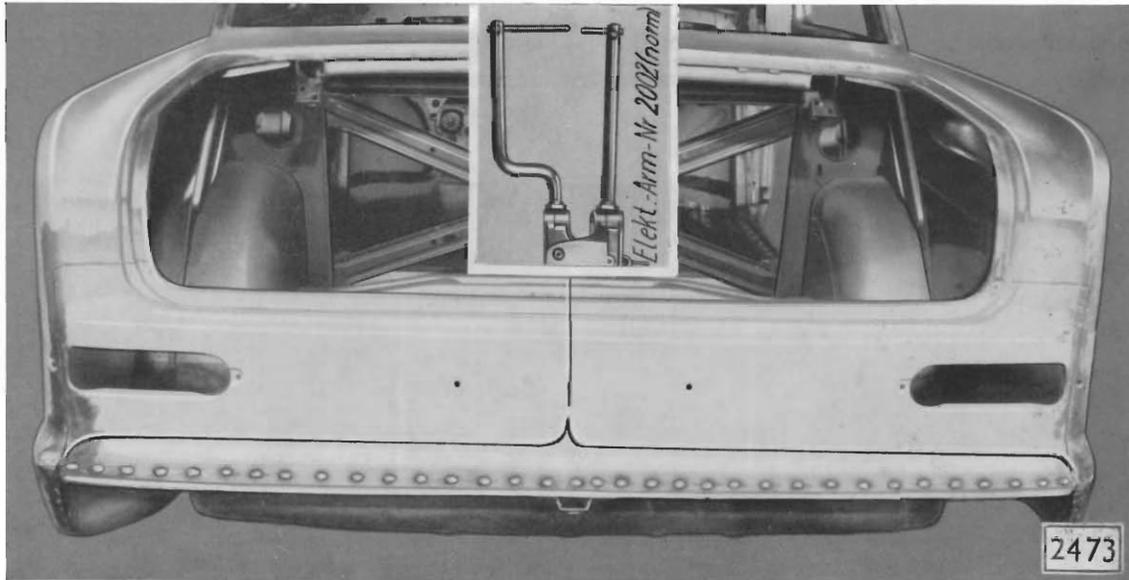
Kofferraumrückwand an Bodenblech zangenpunktgeschweißt
